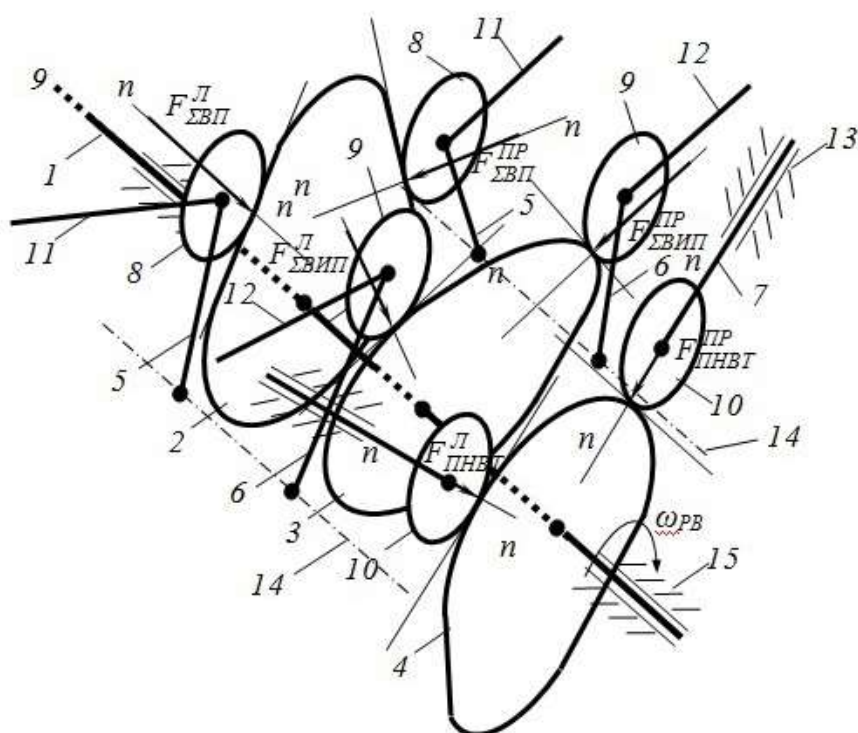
Формування навантажень, діючих на елементи конструкції РВ енергетичної установки тепловоза з дизелем Д49: 1 – розподільний вал; 2 – впускний кулачок; 3 – випускний кулачок; 4 – паливний кулачок; 5 – коромислові штовхачі привода ВПК; 6 – коромислові штовхачі привода ВИПК; 7 – штовхач ПНЕВТ; 8...10 – ролики штовхачів; 11 – штанги привода ВПК; 12 – штанги привода ВИПК; 13 – напрямні штовхачів ПНЕВТ; 14 – осі коромислових штовхачів; 15 – опора РВ
